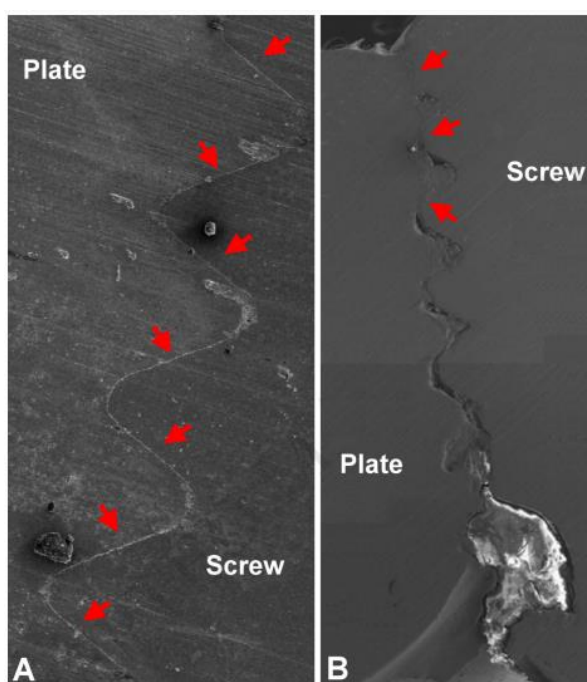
Différents degrés de soudure à froid (flèches rouges) entre la plaque et une vis en titane (x50), A : soudure quasi-complète, B : soudure partielle (Lin et al. 2018).
